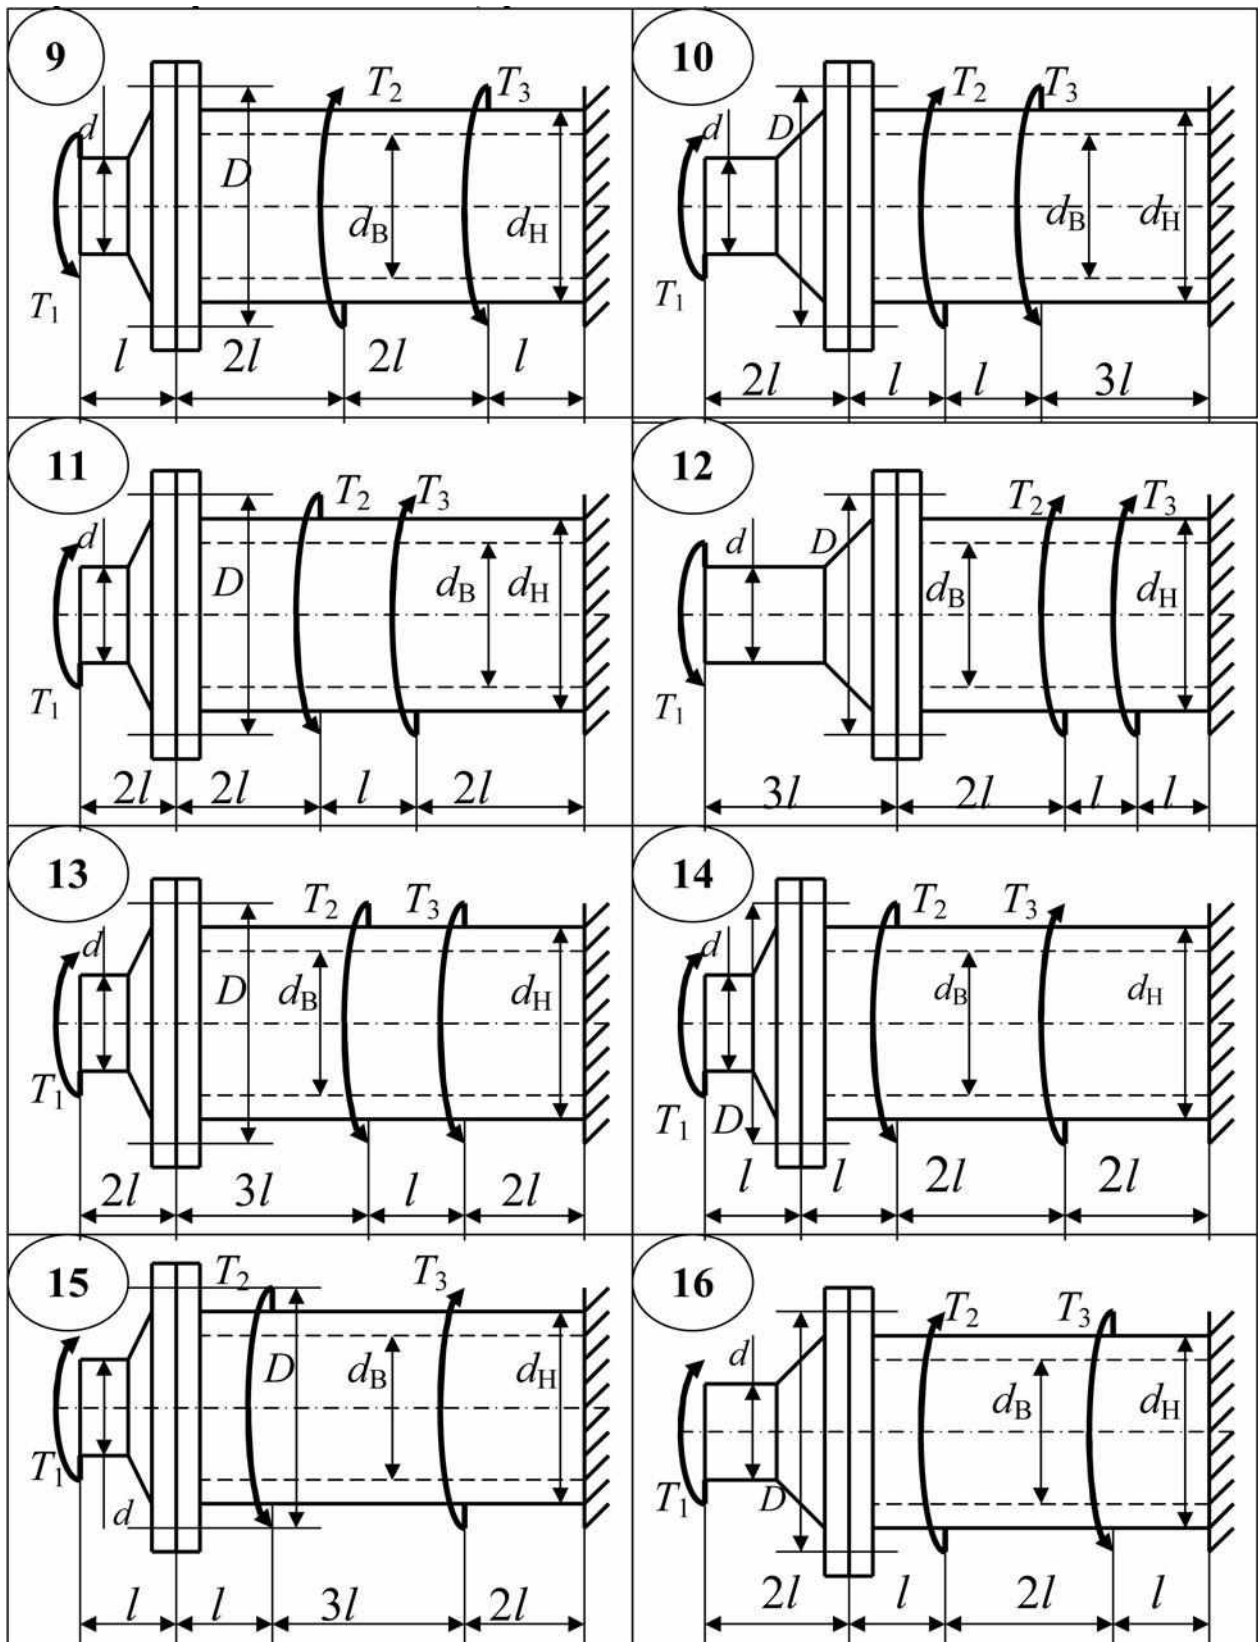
Варианты расчетных схем (9–16) задание 2
